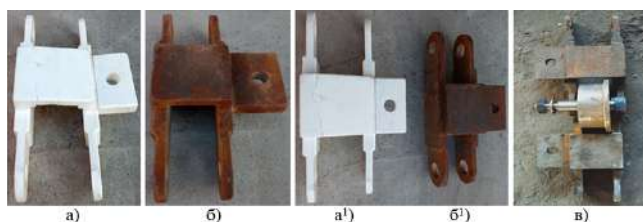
Пеномодели (а,а'), стальные отливки (б,б') и общий вид сборочного цеха шаропрокатного металло-ленточного конвейера (в), используемых в АО «Узметкомбинат».
